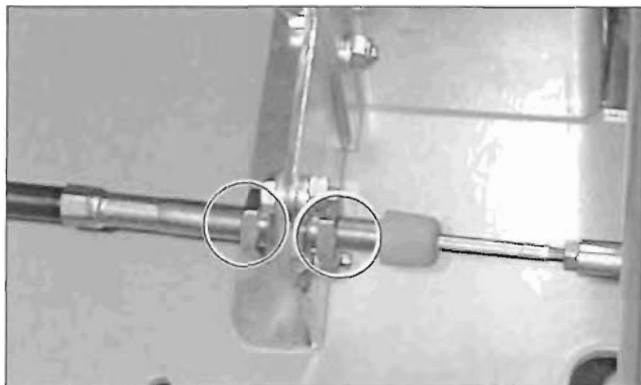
Трос Бодена, контрагайка, регулировочный винт на корпусе редуктора подачи
